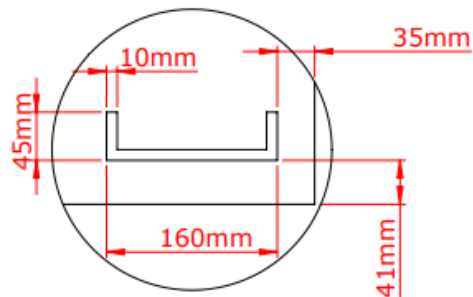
Sección 1B de la carcasa - Detalle de las medidas
